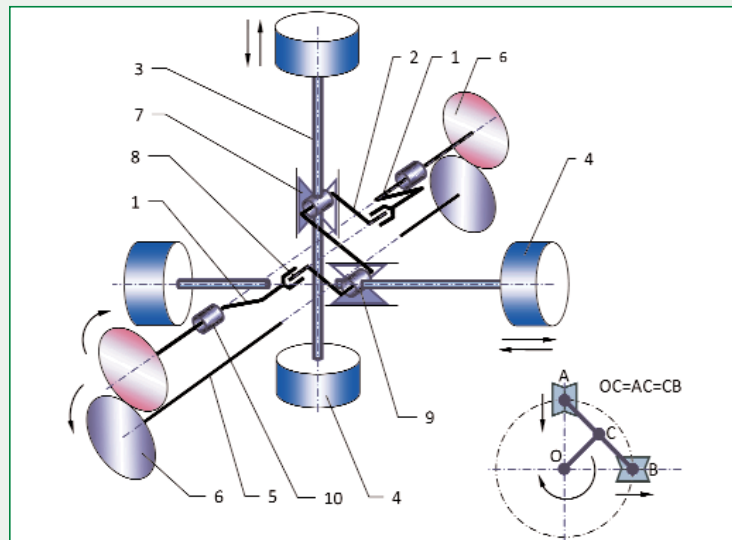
Схема бесшатунного механизма С.С. Баландина с соединительным валом: 1 - водила, 2 - планетарный коленчатый вал (ПКВ), 3 - поршневой шток, 4 - поршень, 5 - синхронизирующий соединительный вал, 6 - синхронизирующая шестерня, 7 - ползун, 8 - опорный подшипник ПКВ, 9 - штоковый подшипник ПКВ, 10 - опорный узел водила
